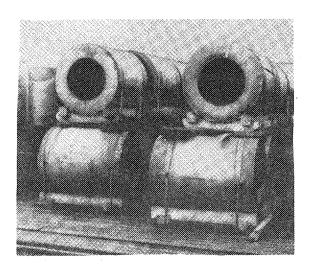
Складирование стального листа в рулонах на "салазках"
